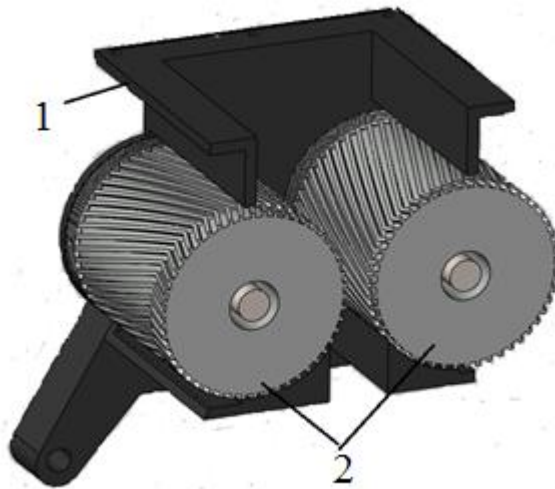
Нагнітальні валки формувальної машини: 1 – робоча камера; 2 – обертові валки з гвинтовими пазами (патент № 111503 UA)
